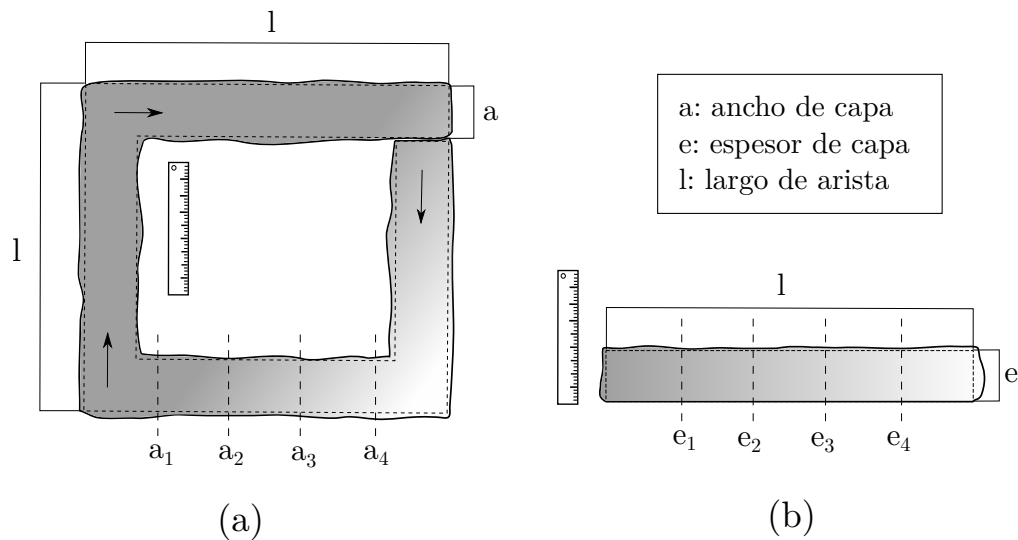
Esquema de ensayo de calidad de extrusión, vista en planta y frontal.
